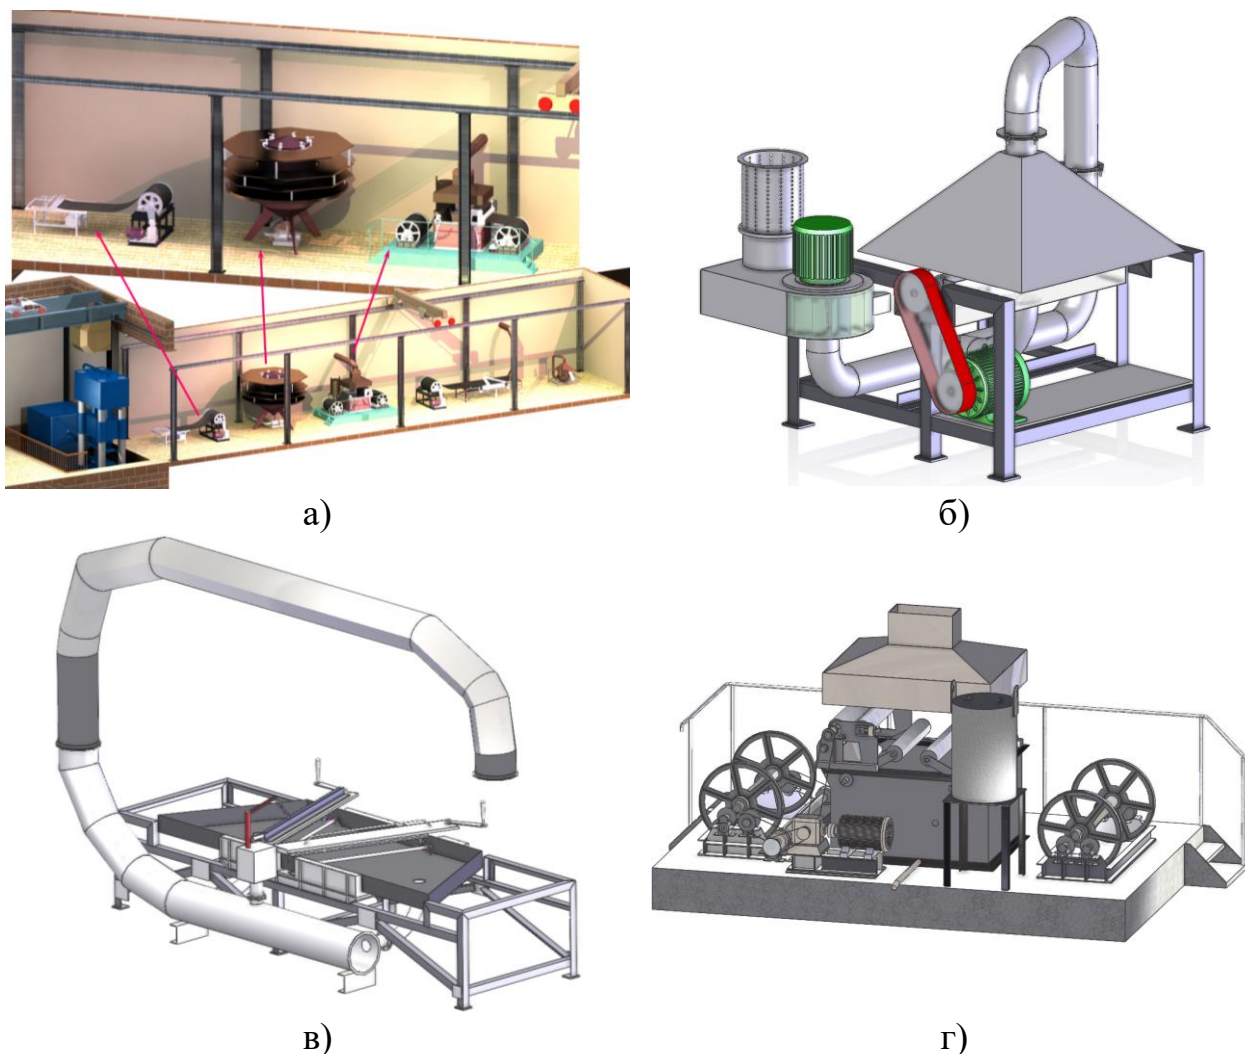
3D-моделі деякого нестандартного обладнання, що використовується в цеху виготовлення фенол-капрону: загальний вигляд цеху (а), вакуум-стіл (б), машина для термоімпульсного зварювання (в), установка для просочення стрічки (г)
